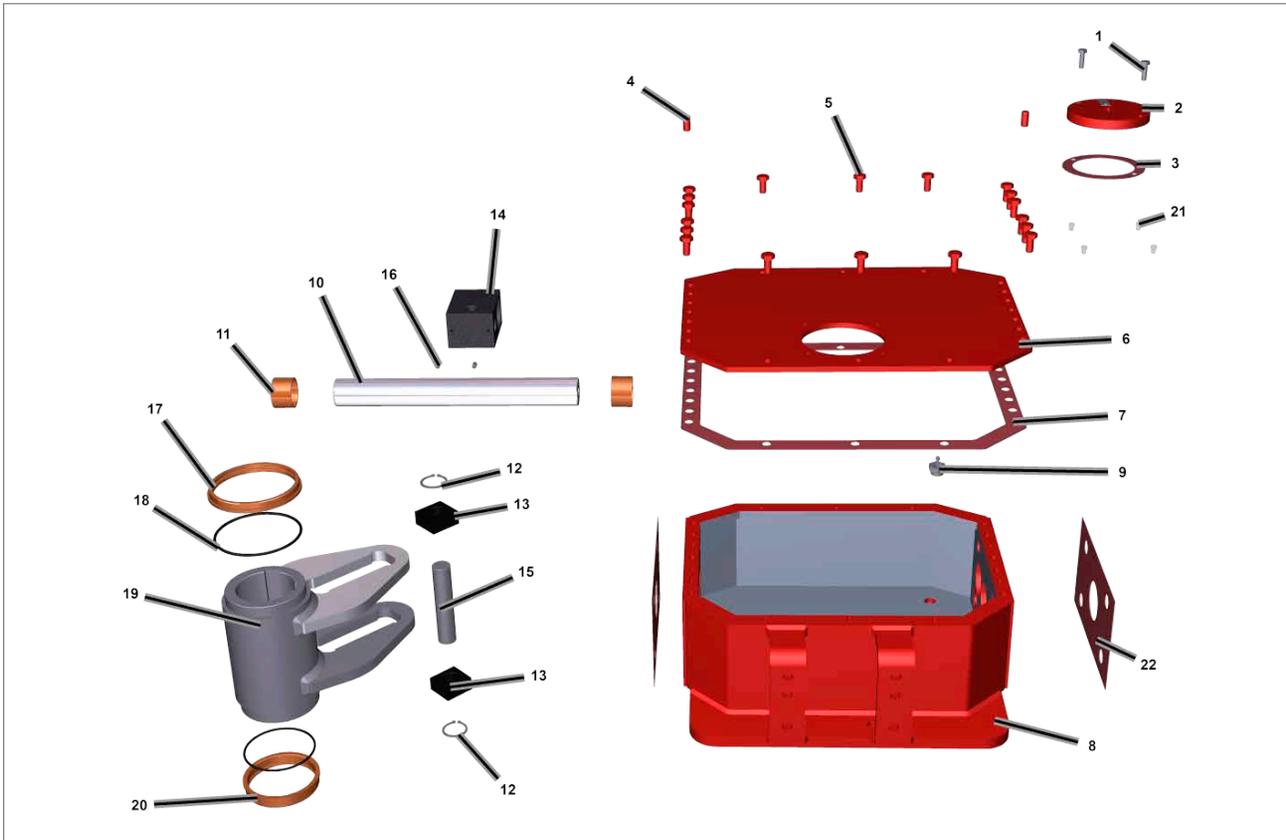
Cuerpo central (soldado) (actuador tamaño 065, 85, 100, 130, 161, 350)
